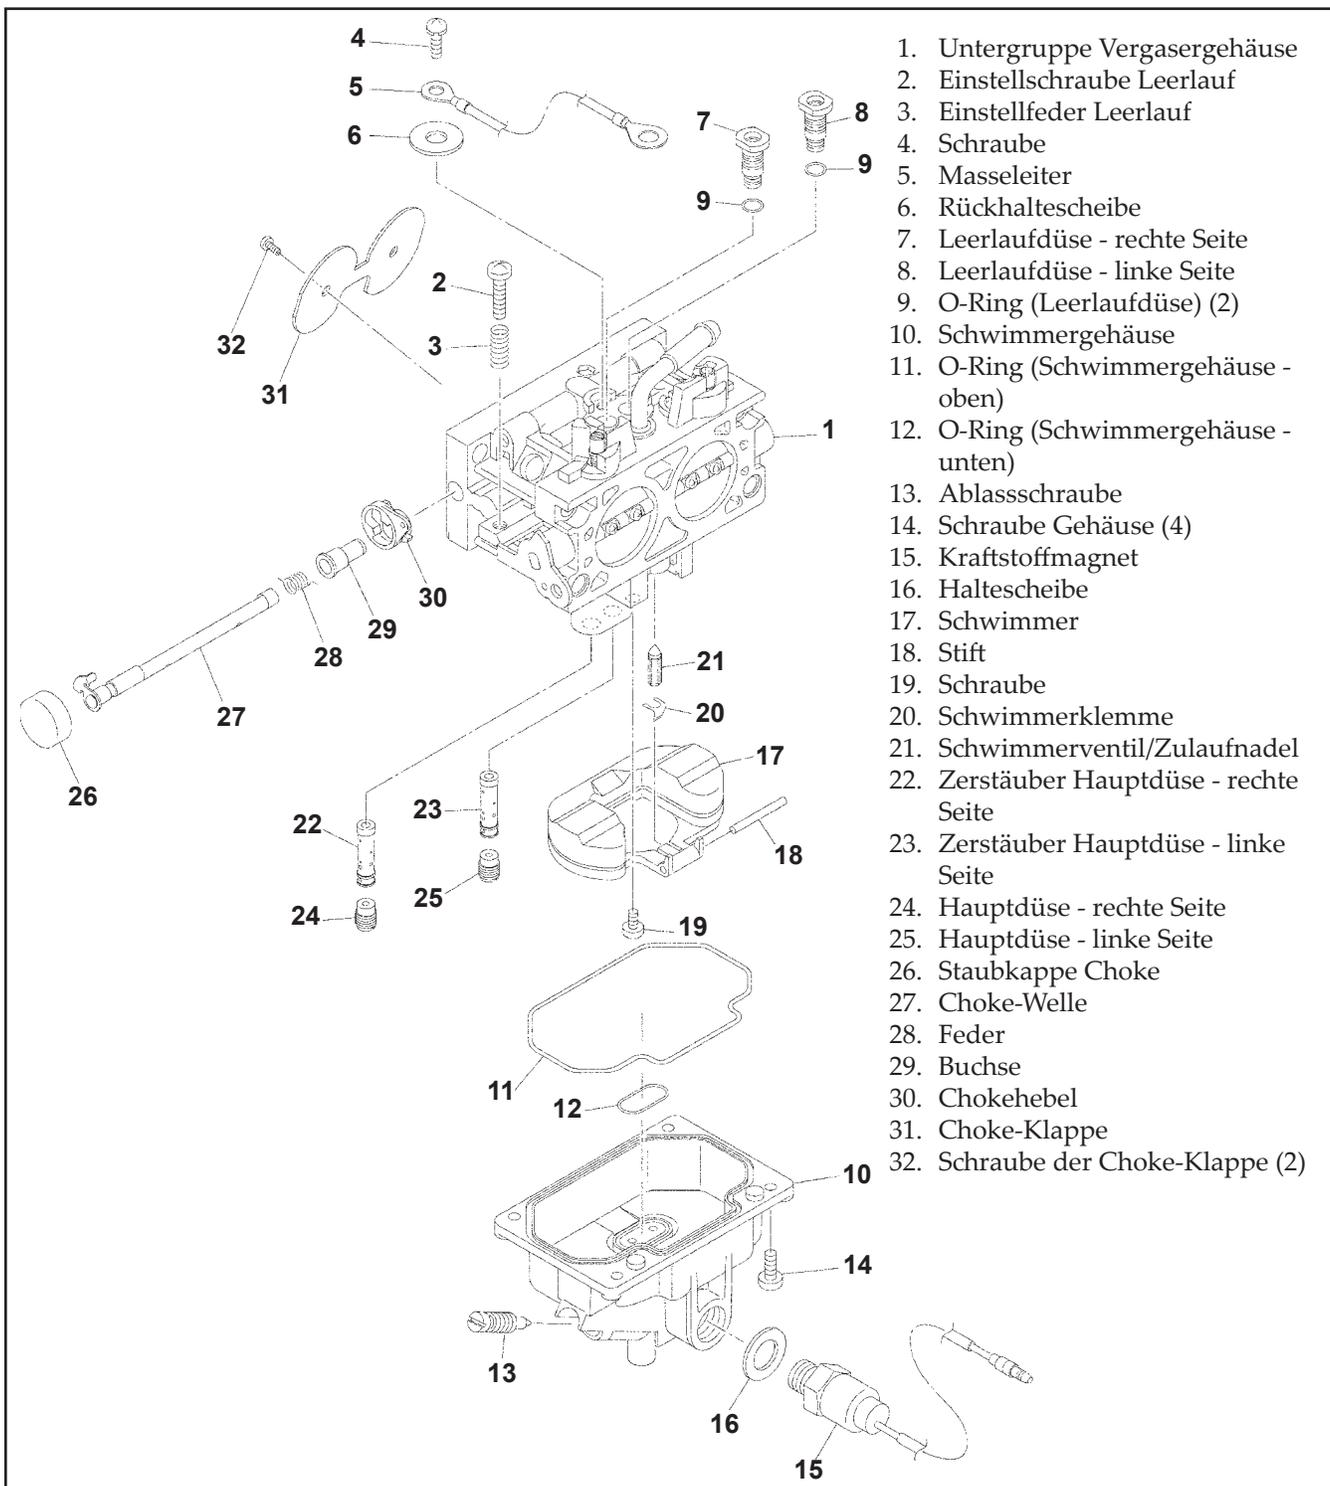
Zweizylindriger Vergaser Keihin BK - Explosionsansicht.
